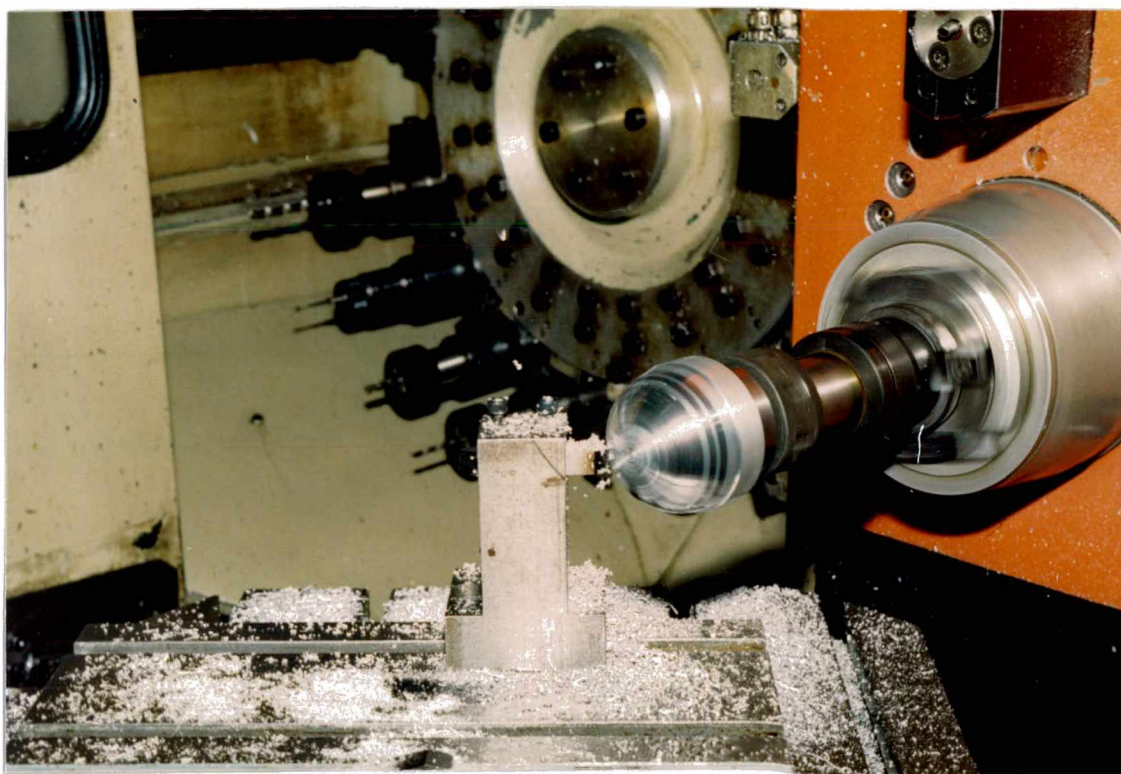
Montagem realizada no centro de usinagem CNC Hüller Hille nb-h 65 para reproduzir o modo torneamento e o método de interpolação.
